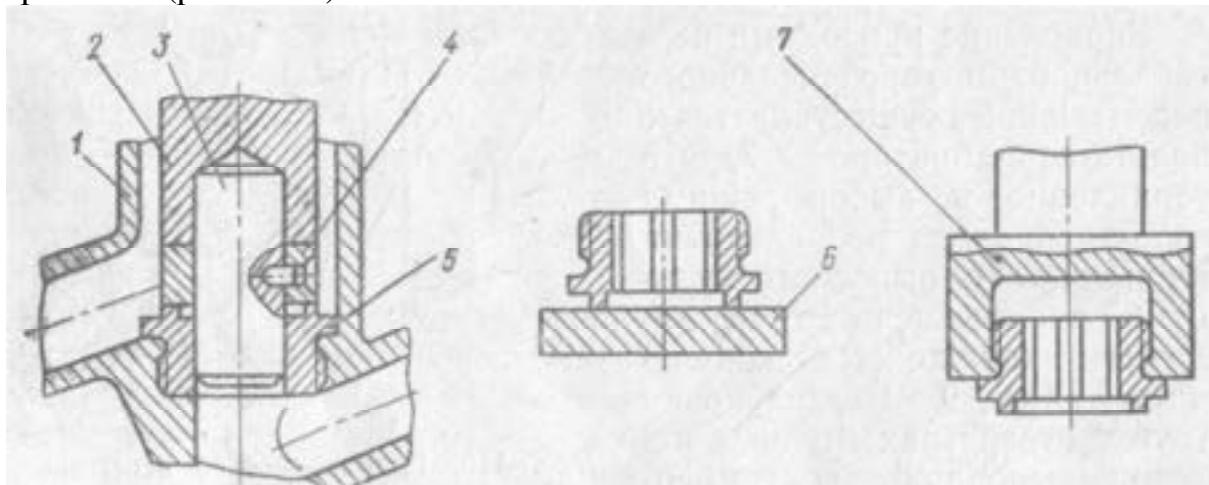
Приспособления для притирки уплотнительных поверхностей седел вентилей:
